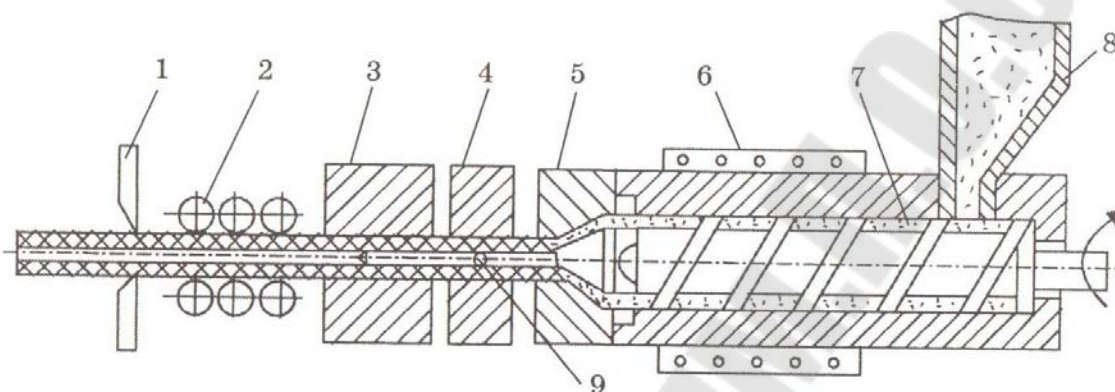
Схема получения труб методом непрерывного выдавливания: 1 – обрезной механизм; 2 – транспортер; 3 – охлаждающее устройство; 4 – калибрующий мундштук; 5 – экструзионная головка; 6 – нагревательные элементы; 7 – рабочий цилиндр; 8 – загрузочный бункер; 9 – дорн
